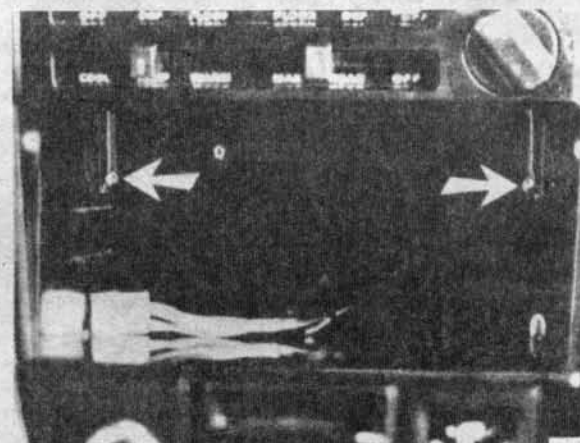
Снятие блока управления системой вентиляции и отопления салона
